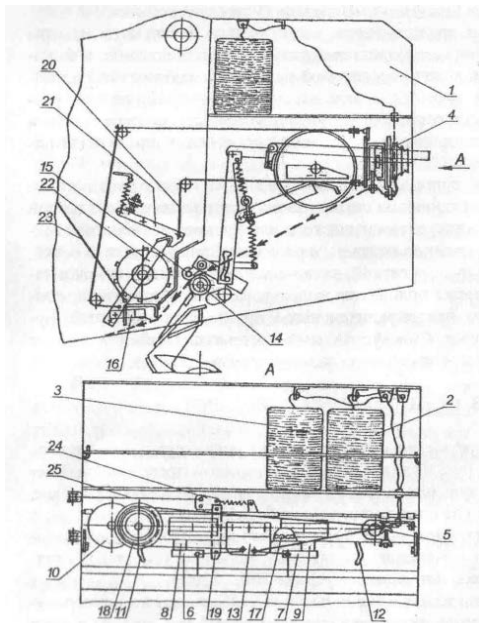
Механизм обмотки рулонов шпагатом: 1 – ящик; 2 и 3 – бабины; 4 – обматывающий аппарат; 5 – тормоз шпагата; 6 и 7 – поводки; 8 и 9 – каретки; 10 – механизм привода кареток; 11 и 12 – ограничители; 13 – кронштейн; 14 – обрезиненный вал; 15 – прижимной ролик; 16 – нож; 17 – цепной контур; 18 – шкив; 19, 22 и 24 – рычаги; 20, 23 и 25 – тяги; 21 – заселка
